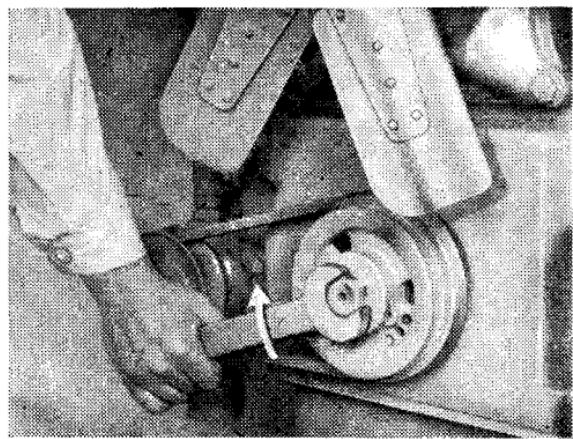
Проворачивание коленчатого вала ключом за болт крепления шкива коленчатого вала
